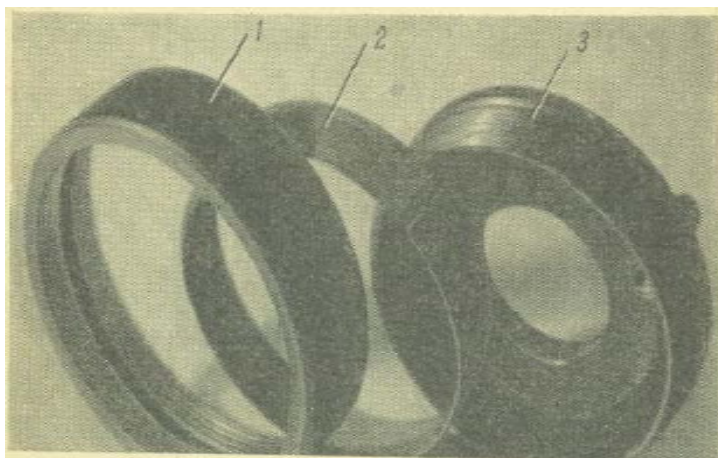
Устройство цаги для головки пружинного привода аппарата „Ленинград“:
